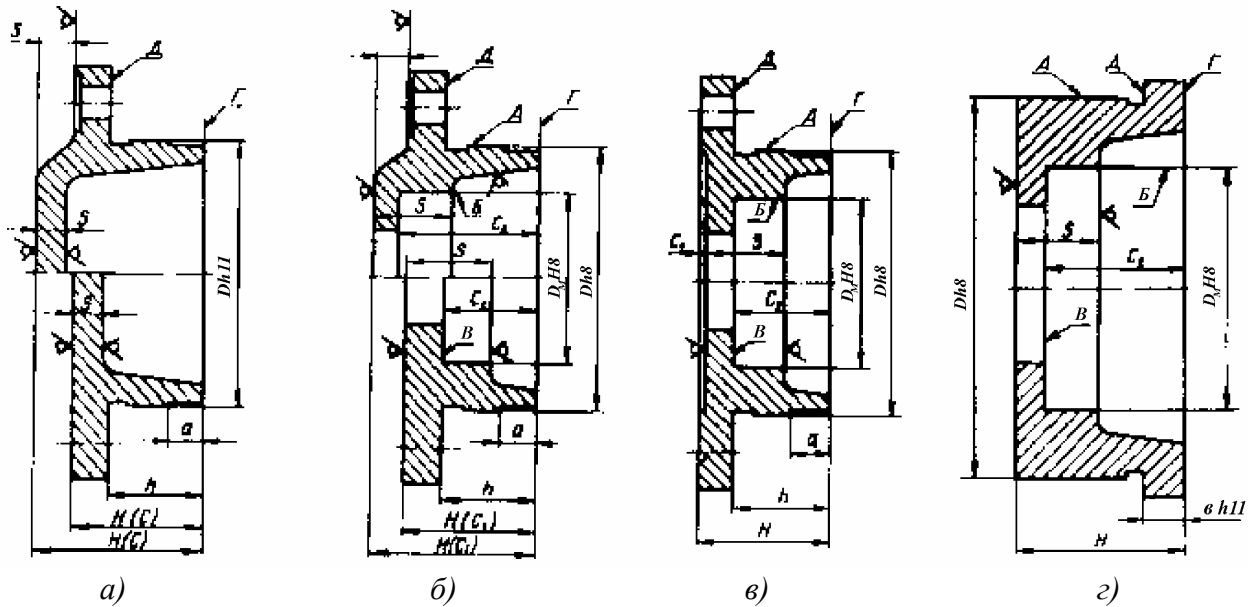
Предельные отклонения размеров и допуски расположения поверхностей, указываемые на рабочих чертежах крышек подшипников
